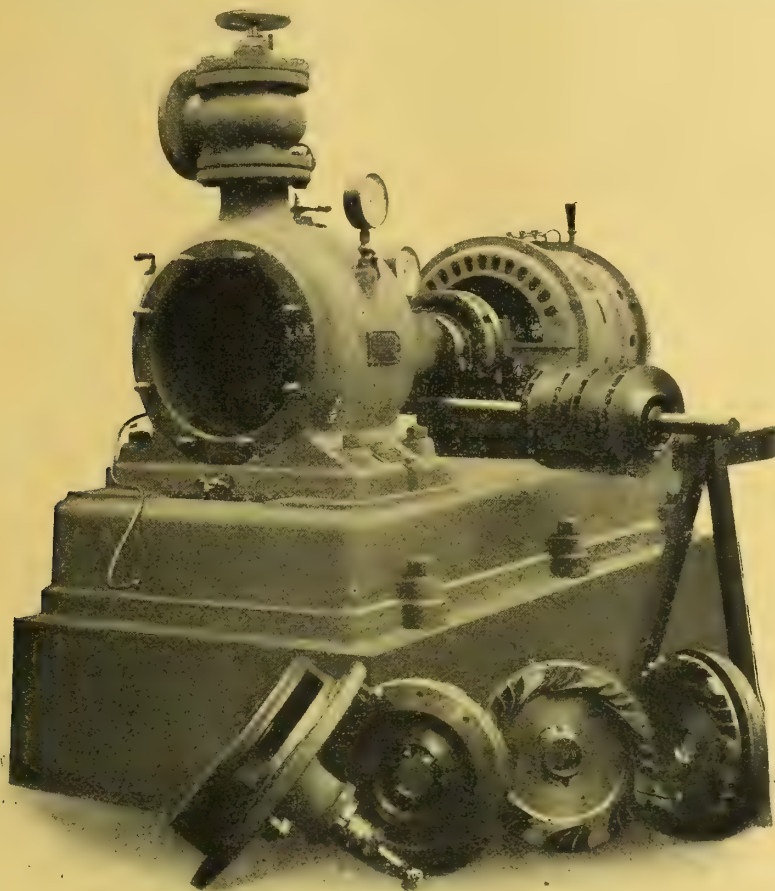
Die Teile der Hochdruckzentrifugalpumpen von Borsig
